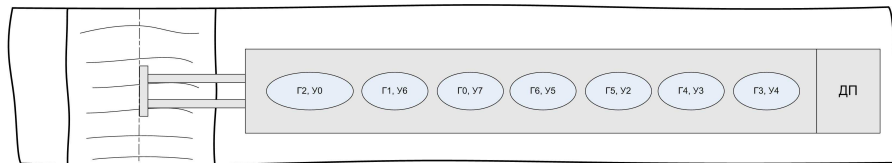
Схема расположения механоакустического блока МАБ1Д относительно сварного шва.
